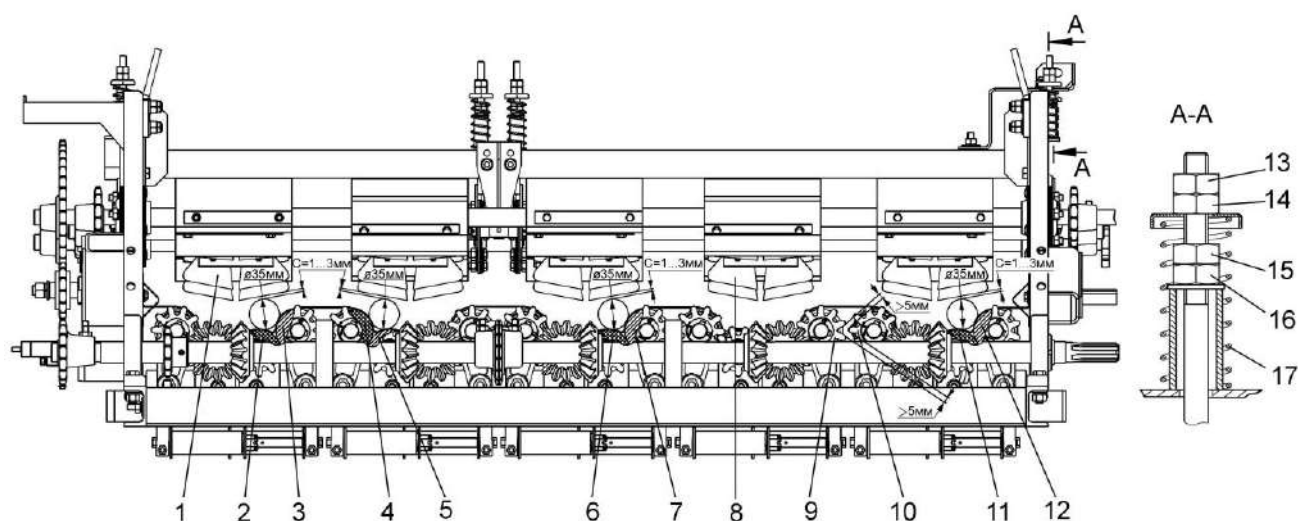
Регулировка натяжения транспортера оберток
